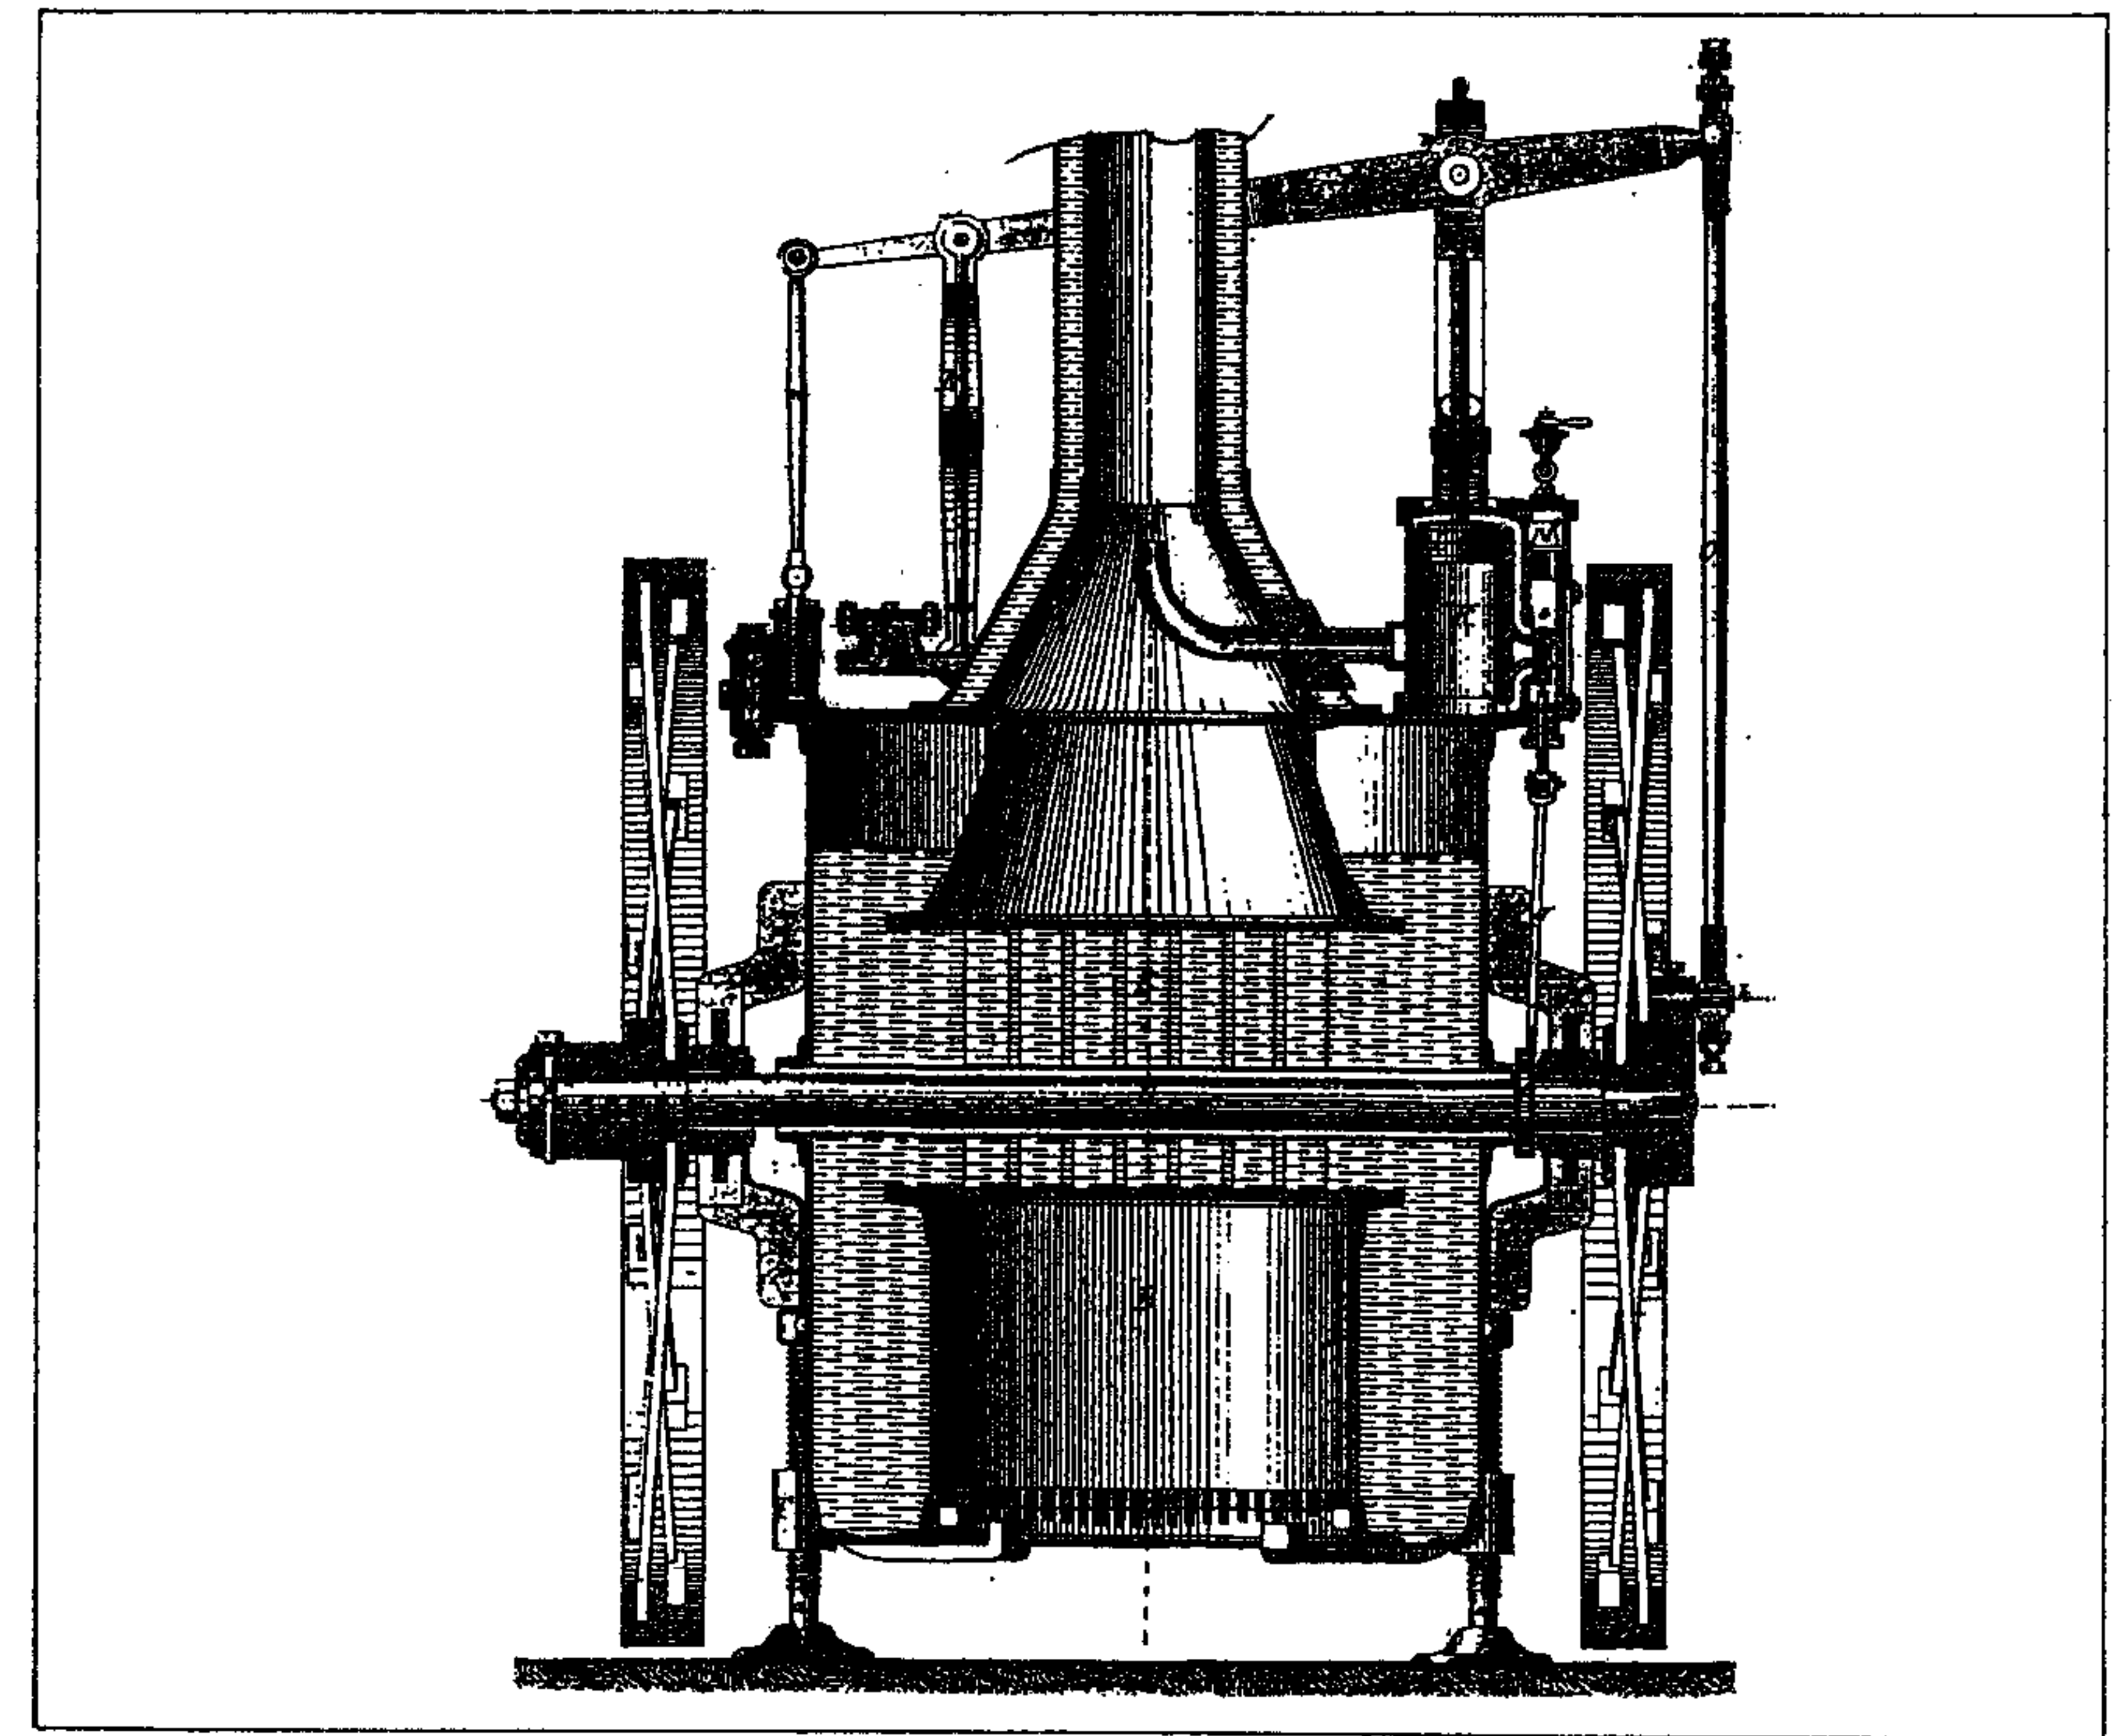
/1: Lokomobilmaschine mit Balancier von Hambruch, Vollbaum & Co (1864)
